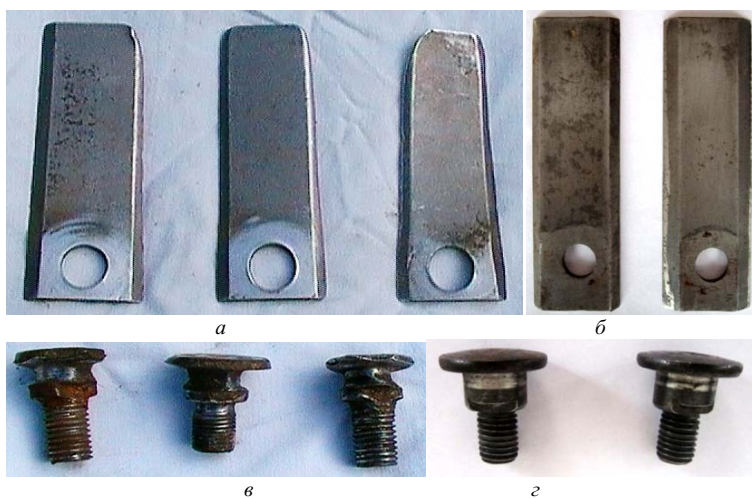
Ножи роторной косилки (*а, б*) и болты крепления ножей к диску (*в, з*)
